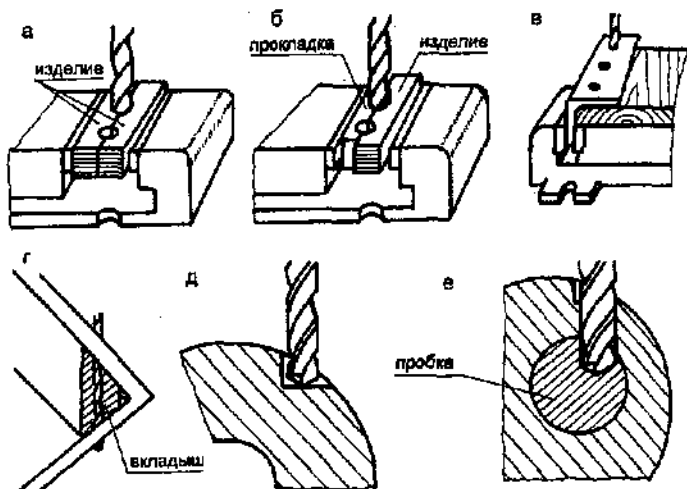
Способы сверления: неполного отверстия (полуотверстия) в изделиях попарно (а); с помощью приставной пластины (б); в — отверстия в уголке; г — в плоскостях, расположенных под углом; д — на цилиндрической поверхности; е — в полых деталях
